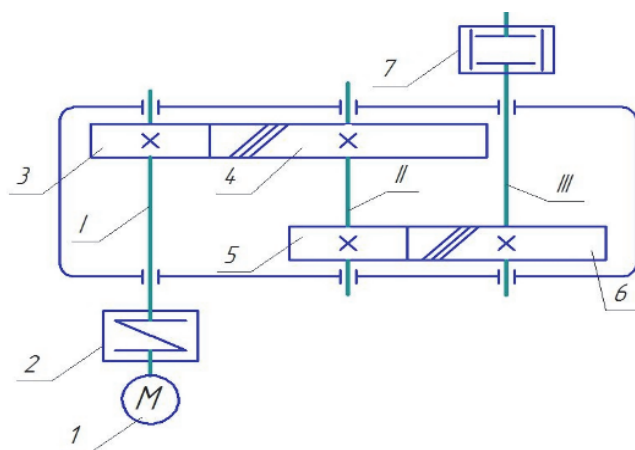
Кинематическая схема привода: 1 – электродвигатель; 2 – упругая муфта; 3 – ведущая шестерня; 4, 6 – зубчатое колесо; 5 – ведомая шестерня; 7 – муфта; I – вал двигателя; II – вал быстроходный; III – вал тихоходный
